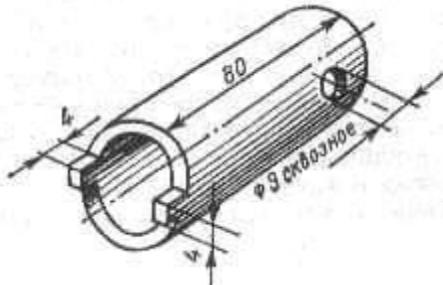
Ключ для гайки чаши подшипника рулевой колонки
